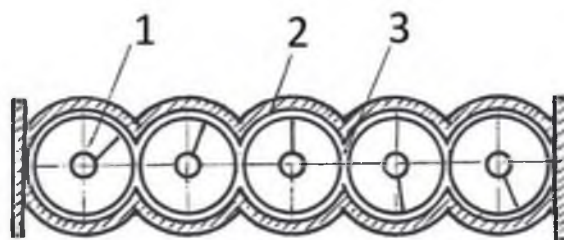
Поперечный разрез пресса: 1 – винт; 2 – кожух; 3 – пресскамера
